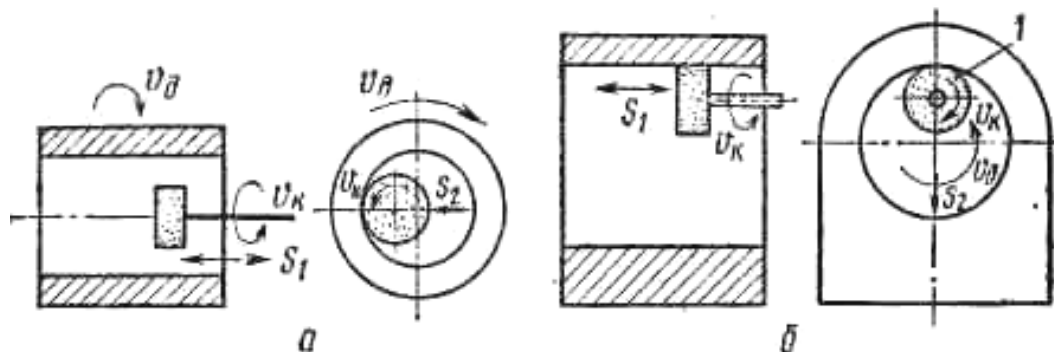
Схемы взаимодействия инструмента и заготовки на внутришлифовальных станках
